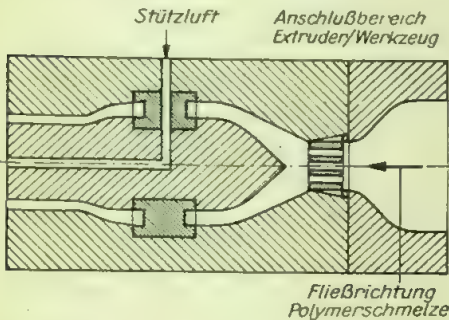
Extrusionswerkzeug für Hohlprofile
